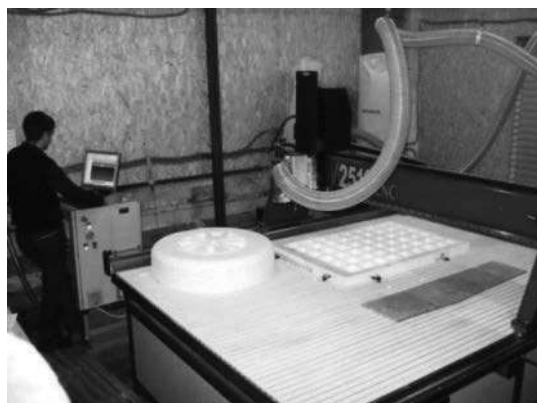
Примеры изготовления моделей для ЛГМ на 3D-фрезерах
